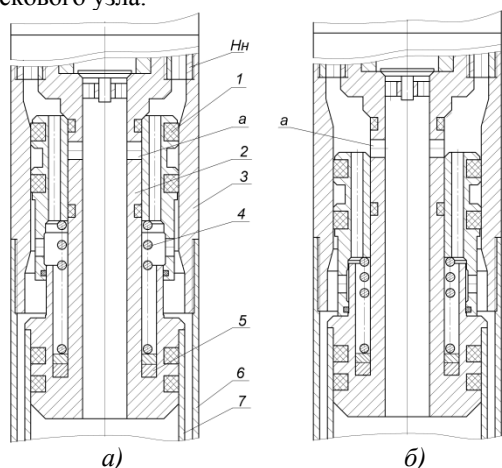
Схема НПУ с распределительным узлом в виде поршня-золотника: 1 – поршень; 2 – шток; 3 – цилиндр; 4 – пружина; 5 – регулировочные кольца; 6, 7 – наружная и внутренняя трубы колонкового набора; «Нн» - нижняя наковальня гидроударника
